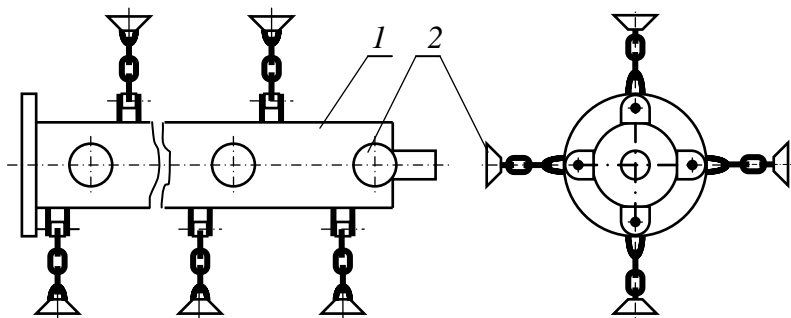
Схема ротора косилки-измельчителя с шарнирно закрепленными чашечными ножами.
